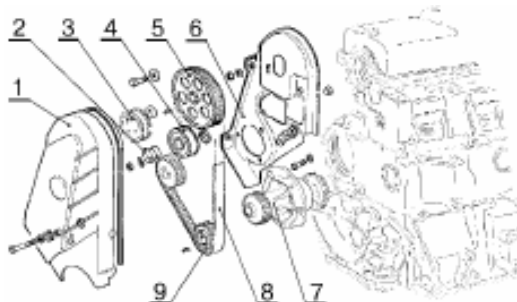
Схема демонтажу деталей приводу газорозподільного механізму.
